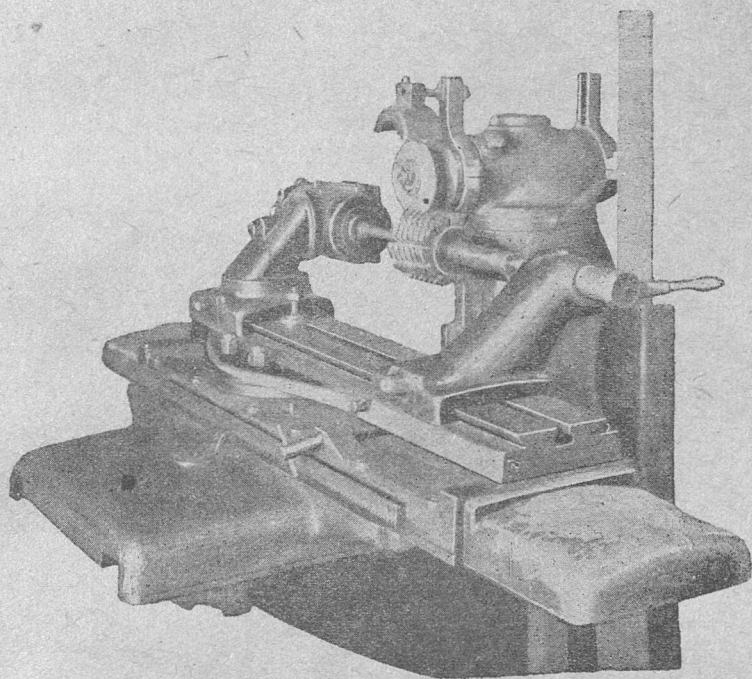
Заточка червячной фрезы на станке Альфред Шютте.
